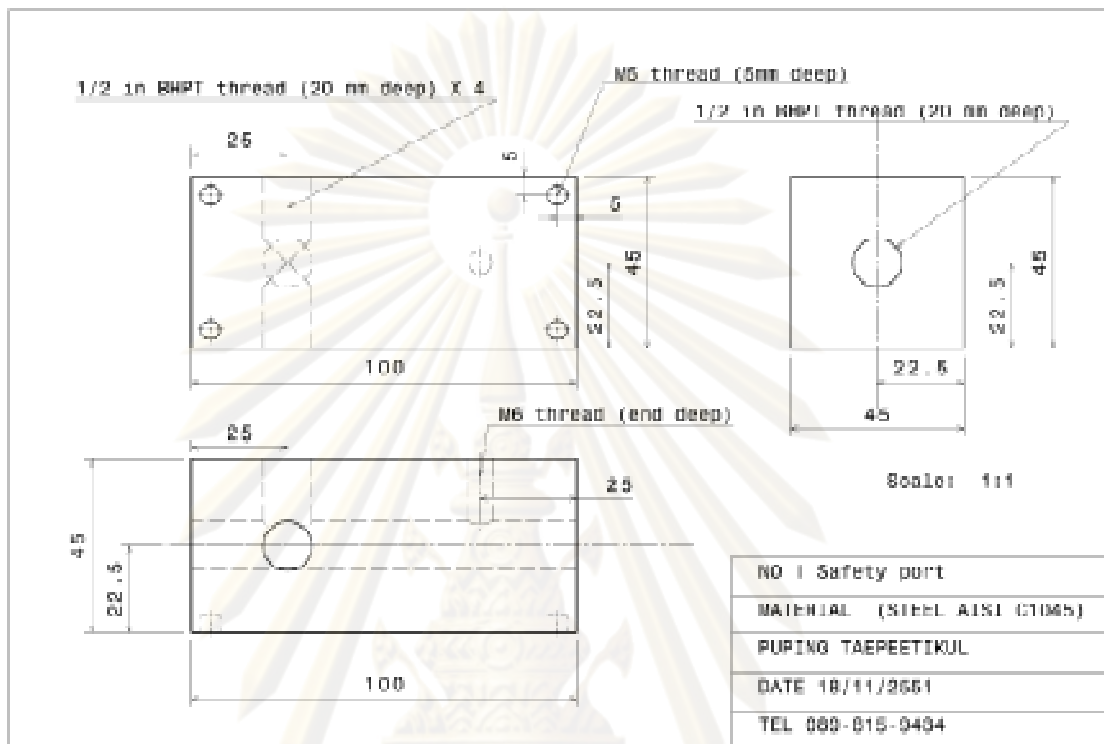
แบบ Drawing (Geometrical detail) ของ MCLP
